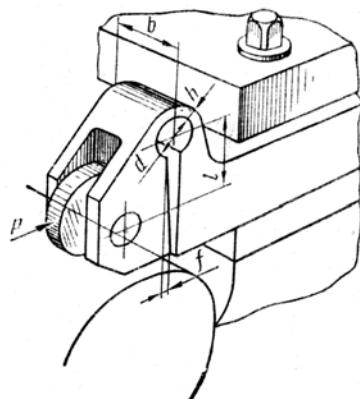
Универсальное однороликовое устройство с пружинящим корпусом
